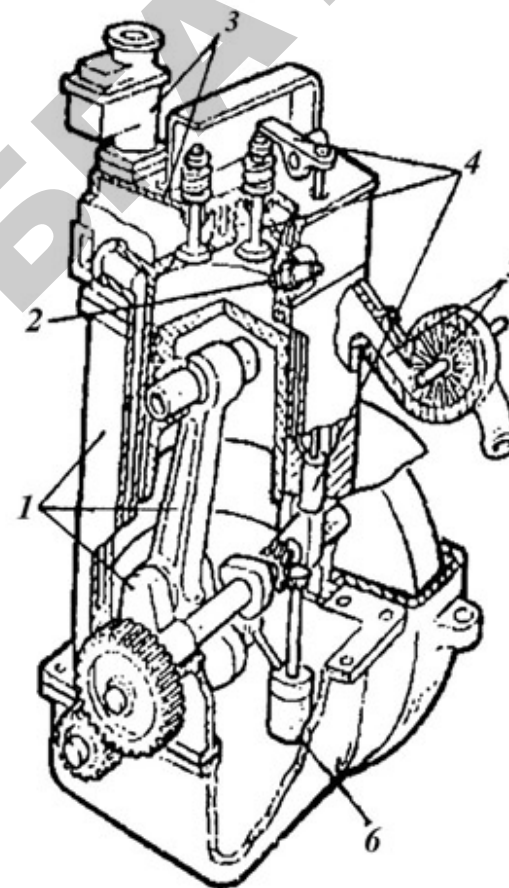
Общее устройство одноцилиндрового двигателя
